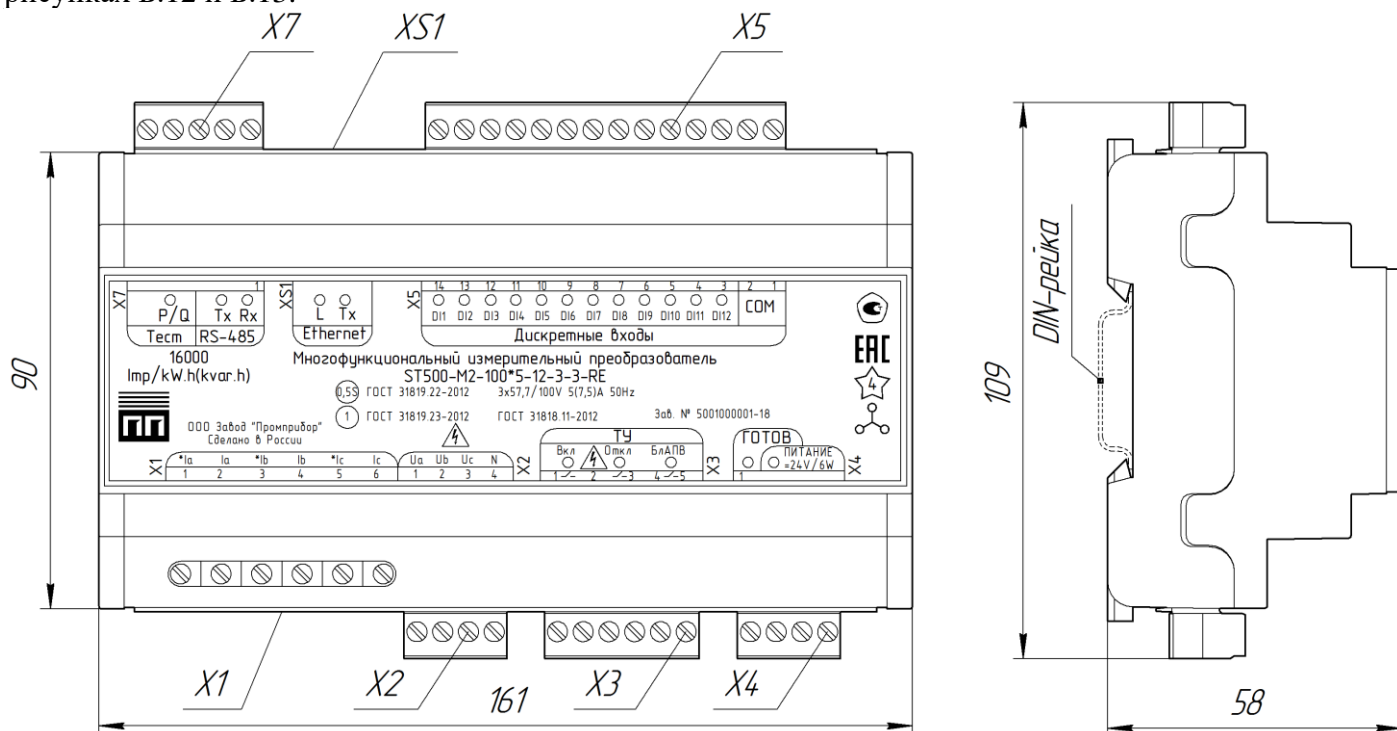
Внешний вид и габаритные размеры МИП
